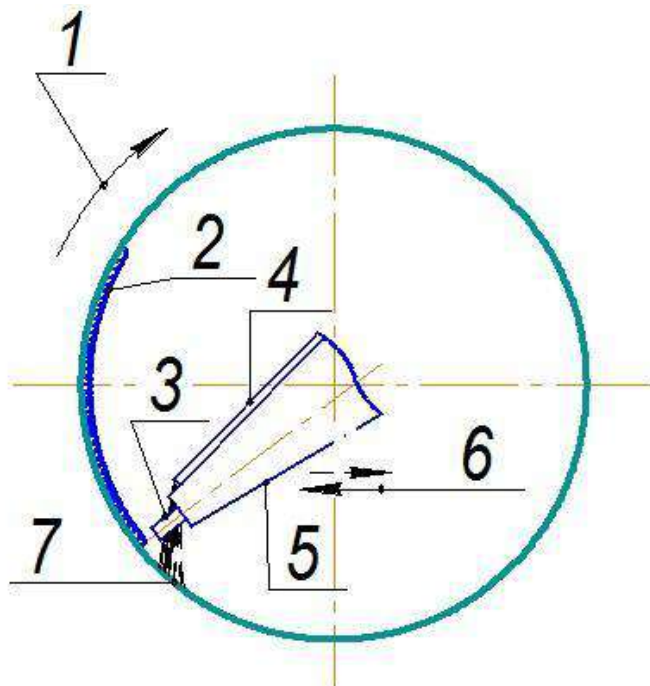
Схема наплавлення внутрішньої поверхні:
